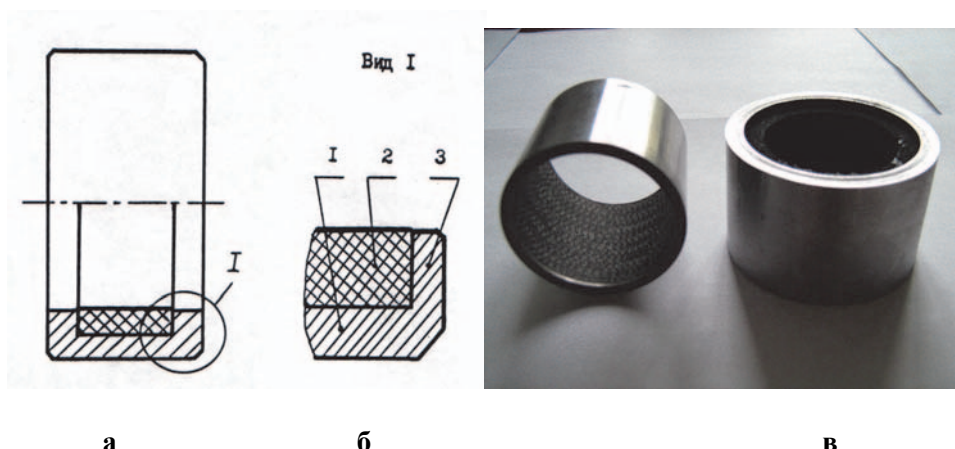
Общий вид втулки шарнирного подшипника скольжения после изготовления (фото авторов): а – основа втулки; б – УУКМ; в – бурт
